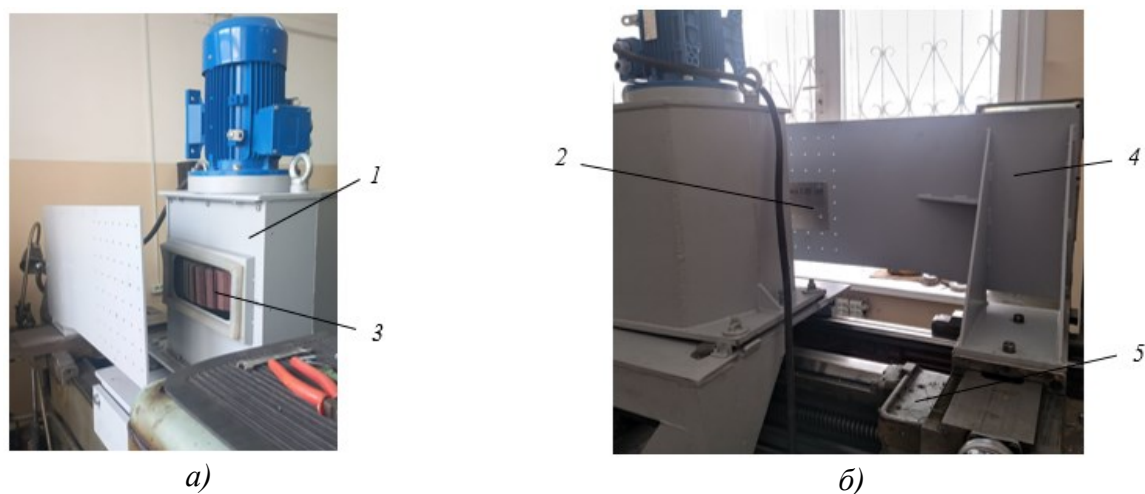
Оборудование для комплексного исследования зачистки лепестковым кругом: 1 – зачистная установка; 2 – образец; 3 – абразивный лепестковый круг; 4 – кронштейн для закрепления образцов; 5 – токарно-винторезный станок 1К62
